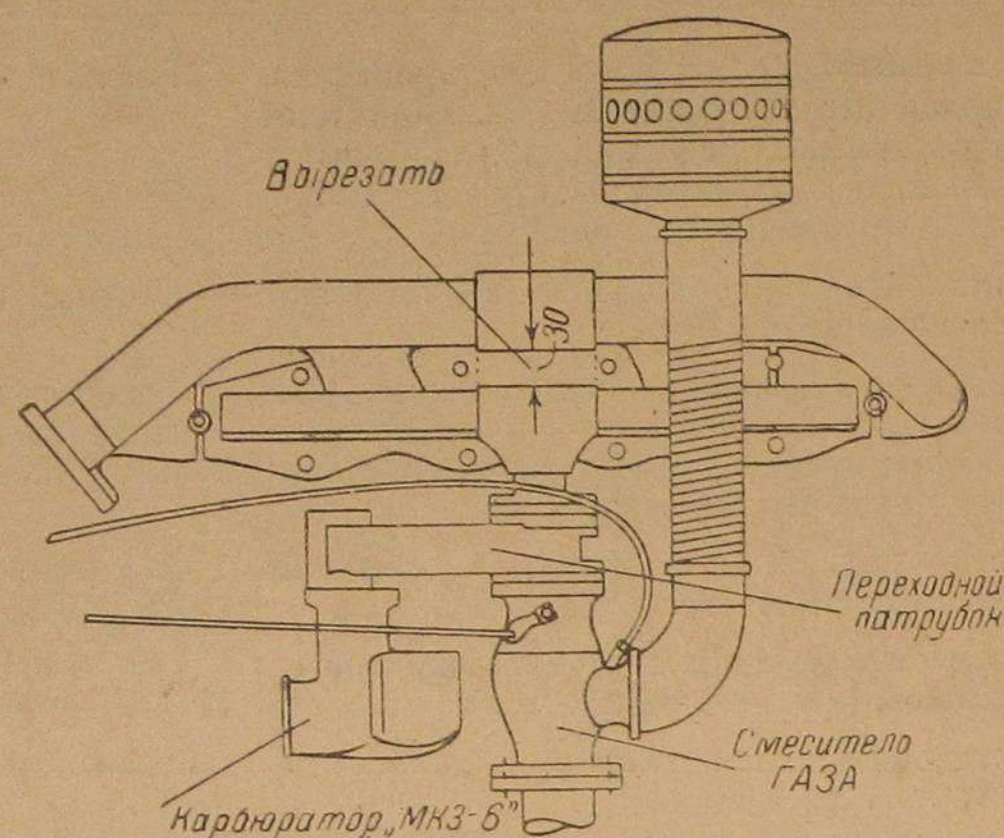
Установка карбюратора МКЗ-6 на газовый двигатель ЗИС-21-А
